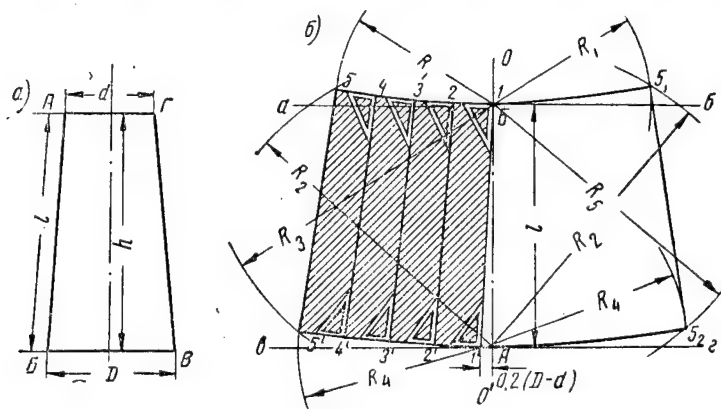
Развертка цилиндрического перехода с недоступной вершиной: а — боковой вид; б — построение развертки.
